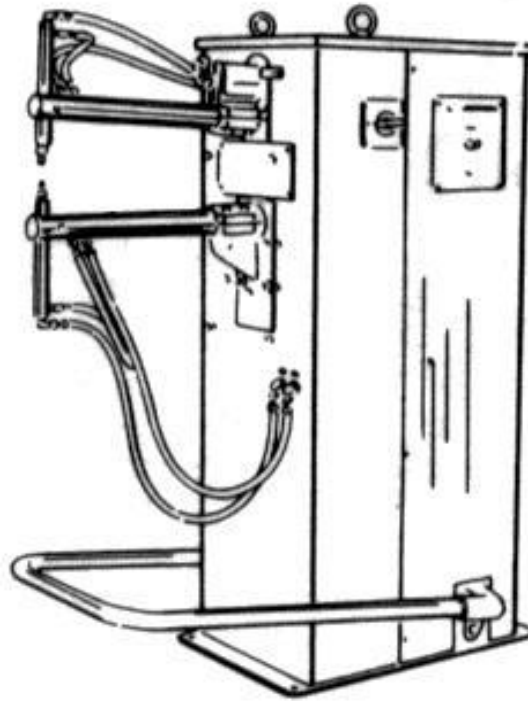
Esquema del proceso de soldadura por puntos (8, 18)
